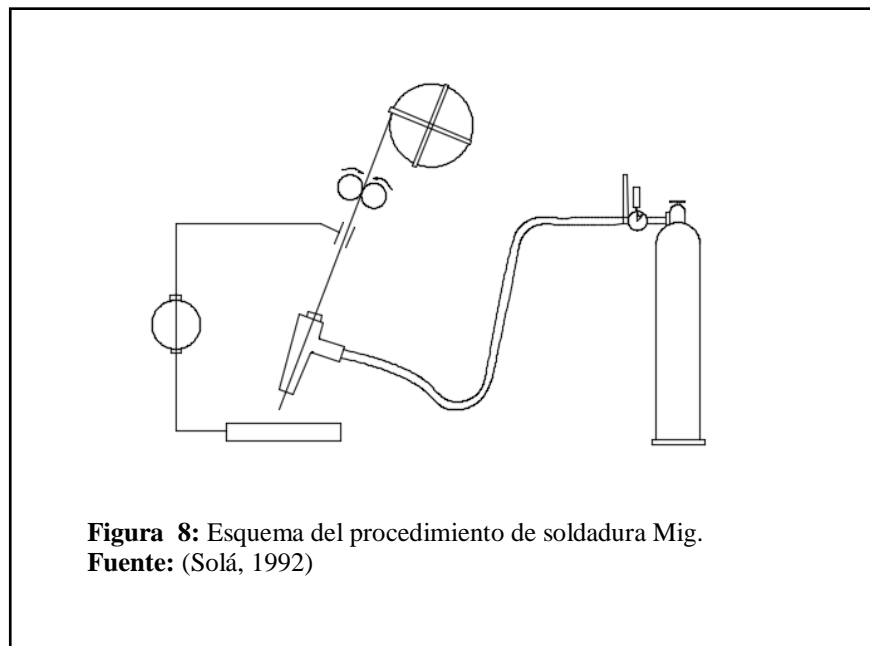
Esquema del procedimiento de soldadura Mig.
